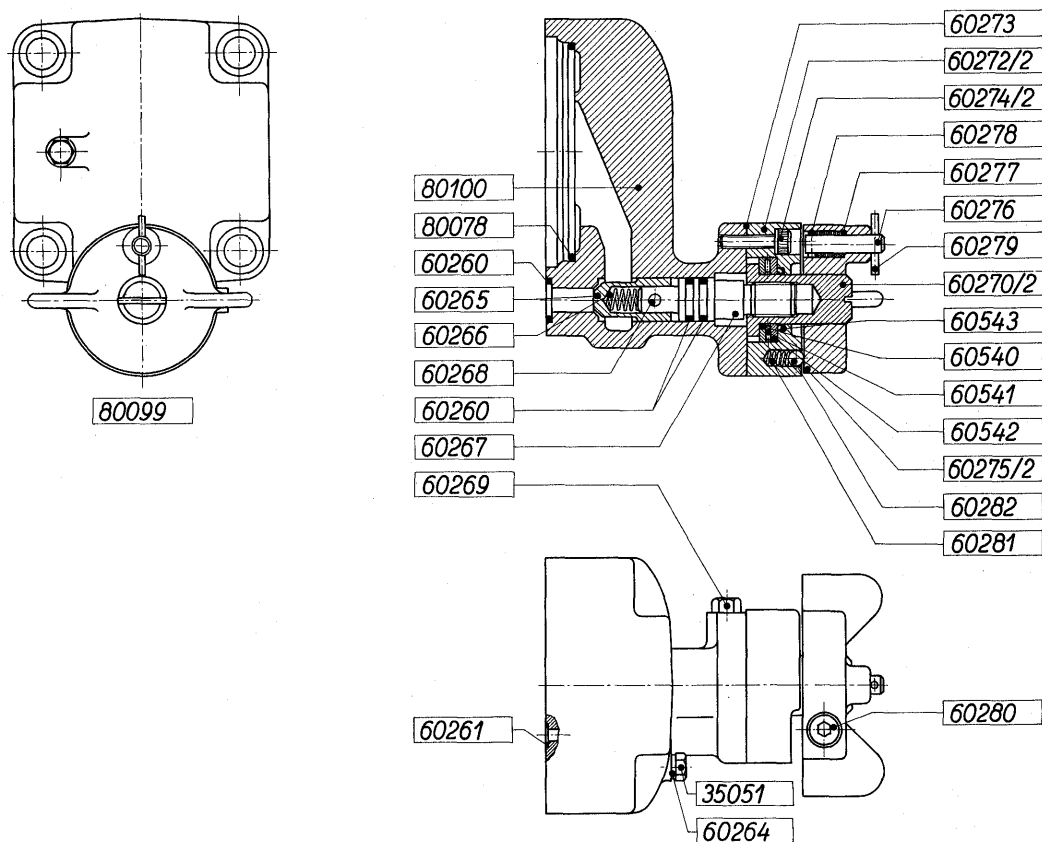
Sænkeventil - komplet - resv.nr. 80099.
